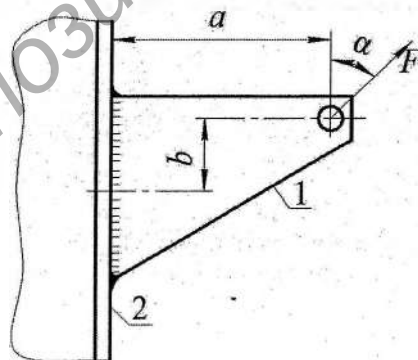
Конструктивная схема сварного соединения
